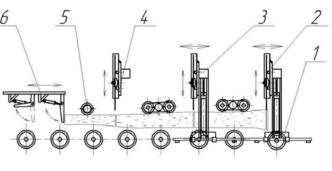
Вид и схема пильного агрегата: 1 — конвейер; 2 — первая подвижная пила; 3 — вторая подвижная пила; 4 — неподвижная пила; 5 — прижимные рычаги; 6 — стопор
